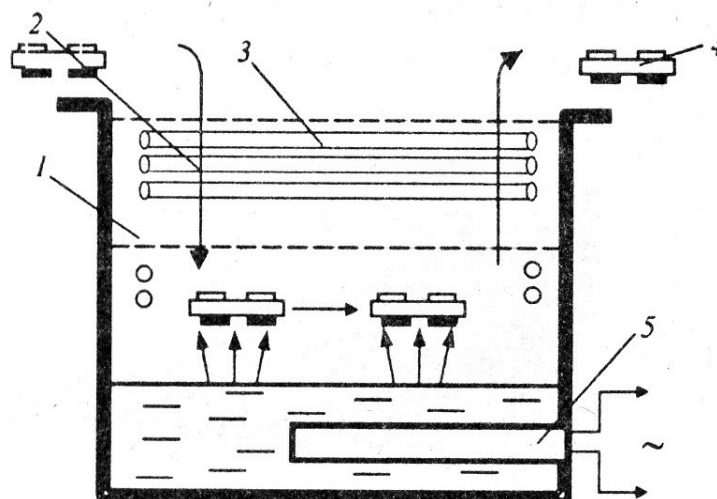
Схема установки пайки в паровой фазе камерного типа.
